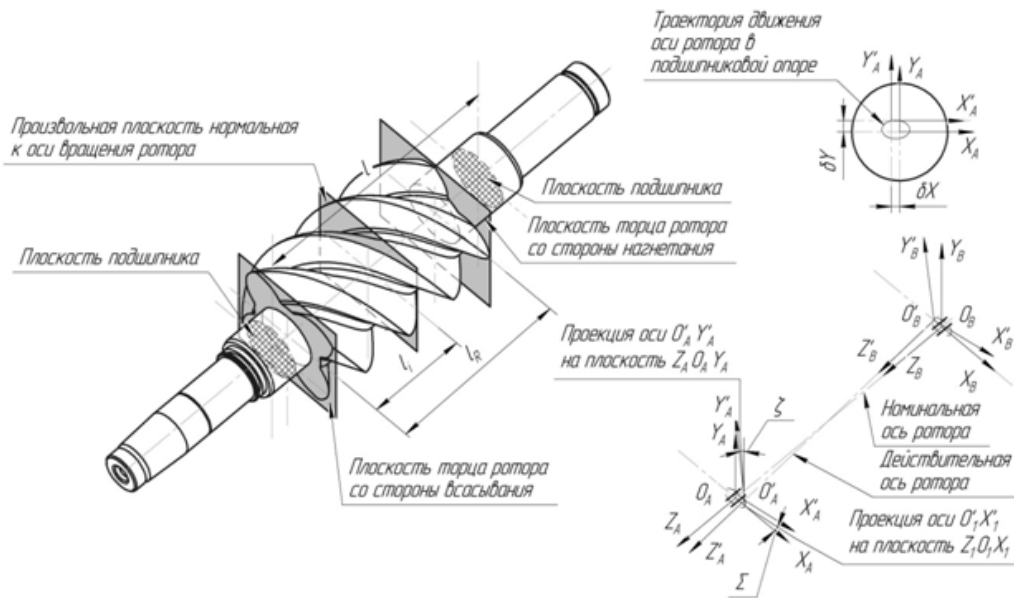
Расчетная схема ротора и его положения в подшипниковой опоре
